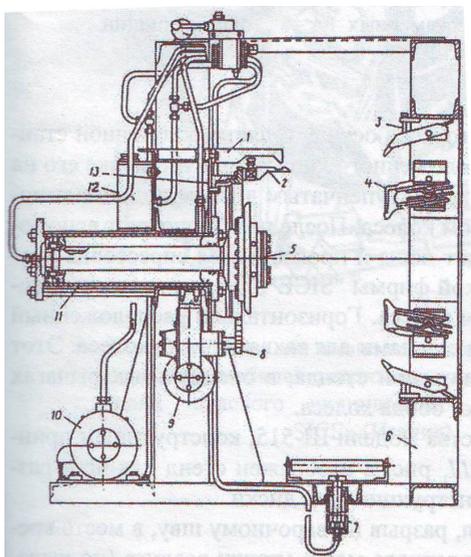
Стенд для монтажа и демонтажа шин колес Ш-509
